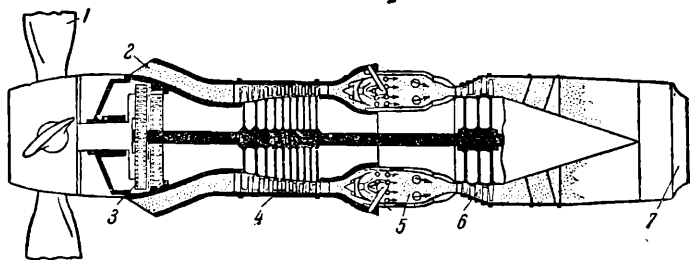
Схема турбовинтового двигателя: 1 — воздушный винт, 2 — воздухозаборник, 3 — редуктор, 4 — компрессор, 5 — камера сгорания, 6 — турбина, 7 — сопло.
